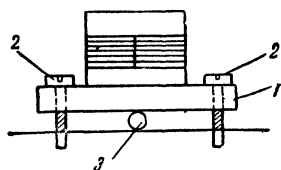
Простое устройство для поворачивания головки: 1 — поворотная площадка; 2 — регулировочные винты; 3 — стальной опорный шарик
